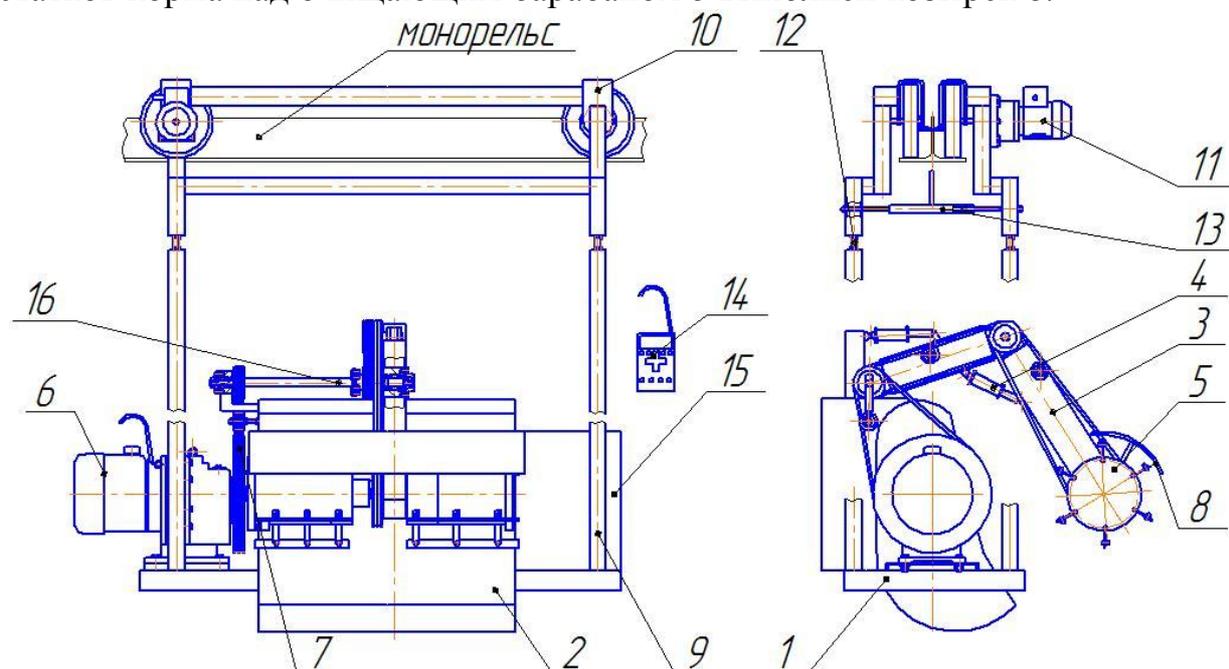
Устройство для очистки кормушек: 1-рама; 2-бункер для остатков корма; 3-стрела; 4- гидравлические цилиндры; 5-барабан очищающий; 6-мотор-редуктор; 7-передача ременная; 8 - козырек; 9 - стойка; 10 - тележка; 11 - мотор-редуктор; 12-проставка демпфирующая; 13-стяжка; 14 - пульт управления; 15 - элементы управления; 16 – вал.
